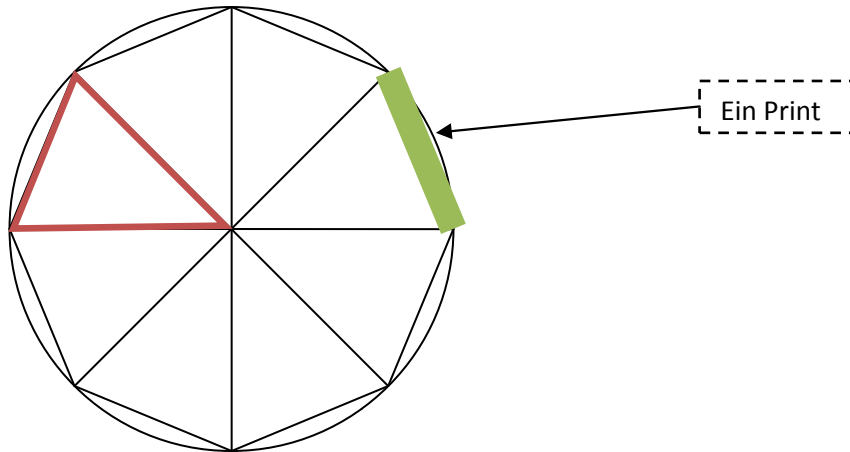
Skizze der Obenaufsicht auf den Flansch
